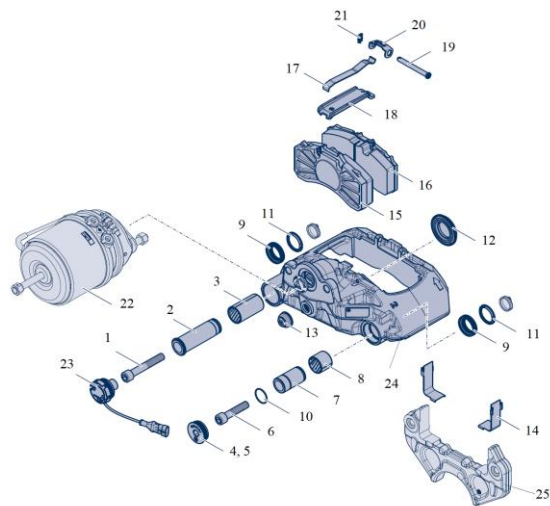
Общий вид тормозного механизма BPW с пневмокамерой
